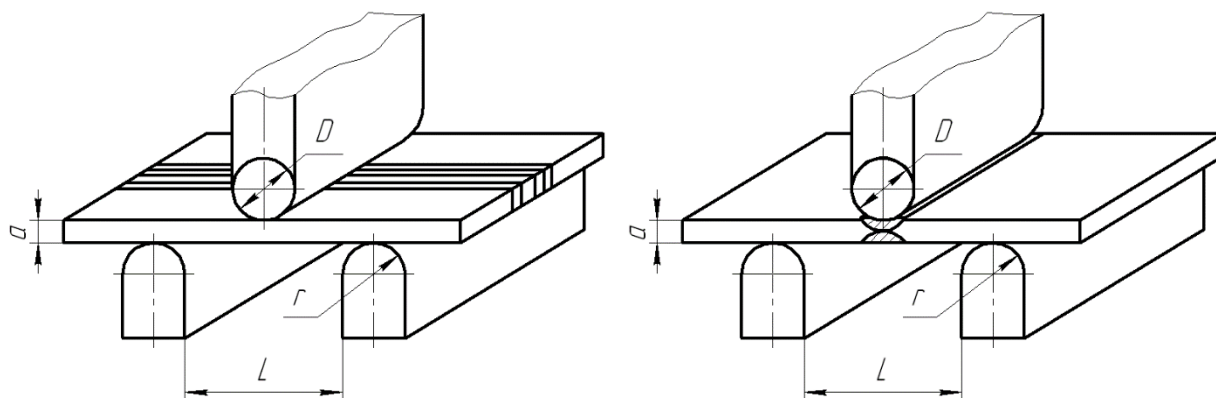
Схема испытания сварного соединения на изгиб
